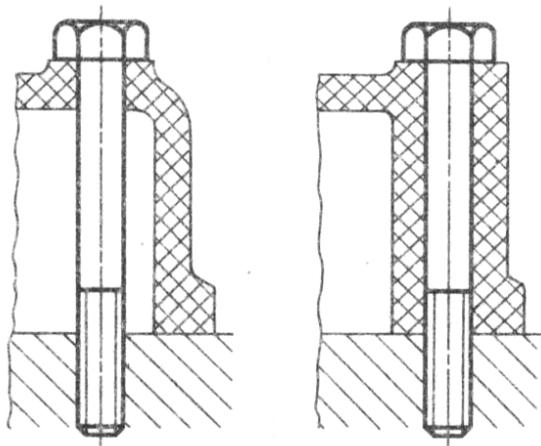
Разгрузка детали от изгиба силой затяжки
